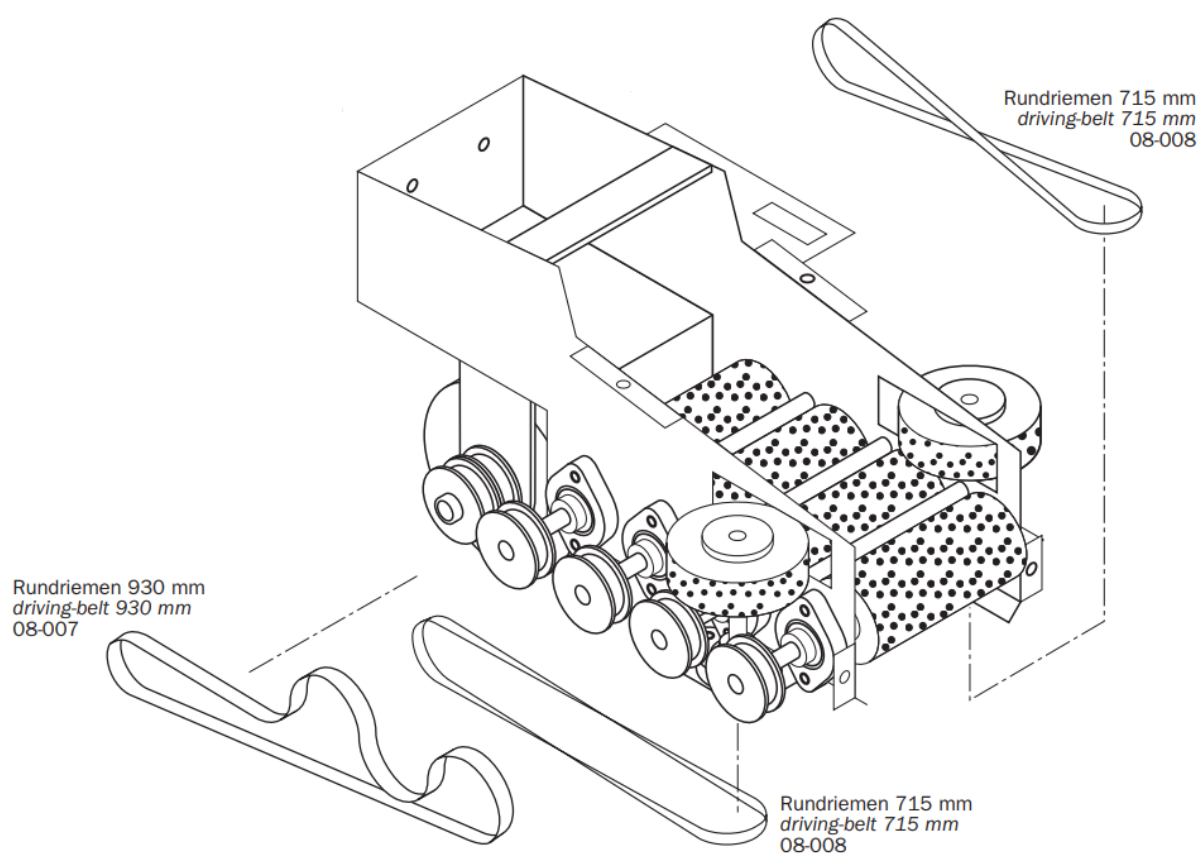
Datasheet Sole Cleaning machine DRY 90 [2]
